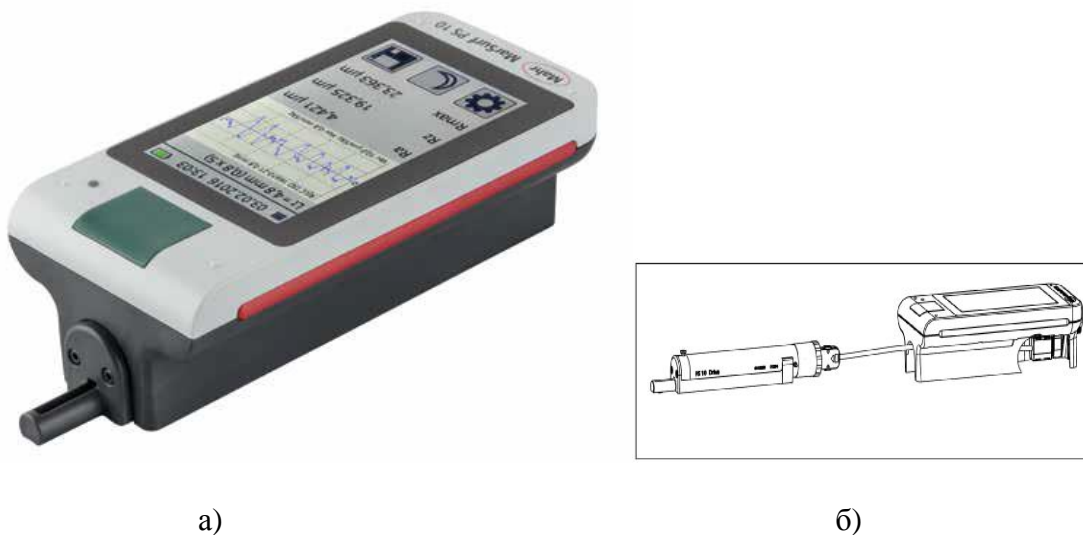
Общий вид прибора для измерений шероховатости поверхности MarSurf PS 10
